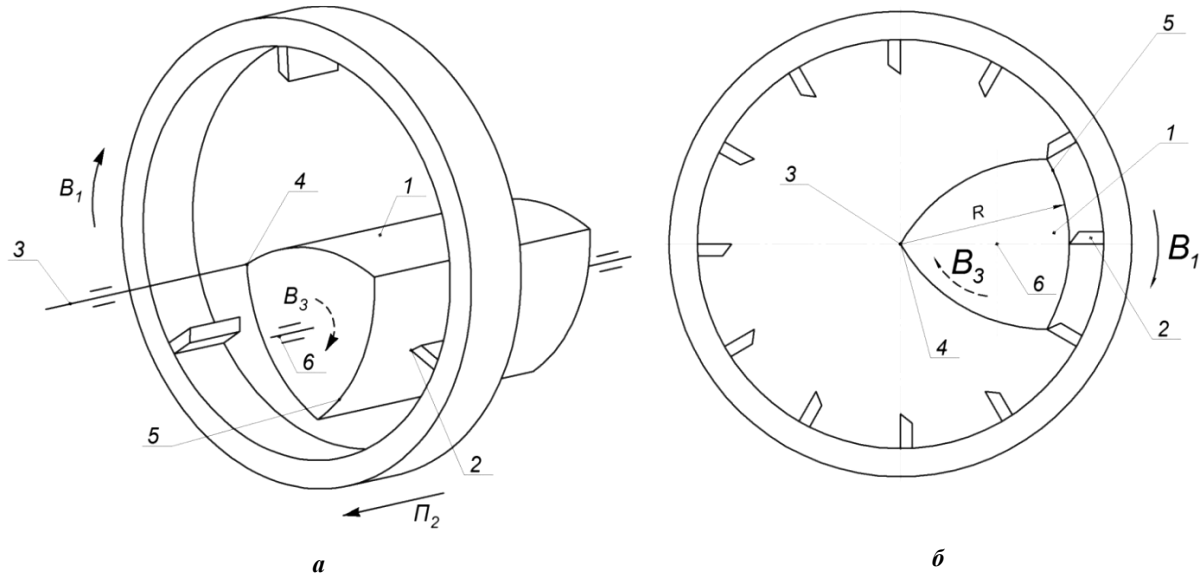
Кинематическая схема обработки (а) и схема формирования профиля детали в виде треугольника Рело (б) охватывающей резцовой головкой
